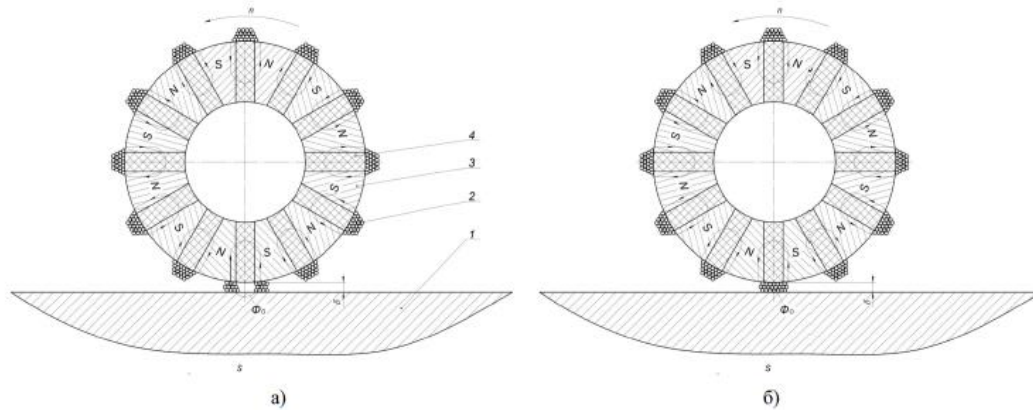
Схема процесу магнітно-абразивної обробки: а) обробка магнітних заготовок; б) обробка немагнітних заготовок. 1 – заготівля; 2 – порція магнітно-абразивного порошку; 3 – магнітопровід; 4 – магніт.
